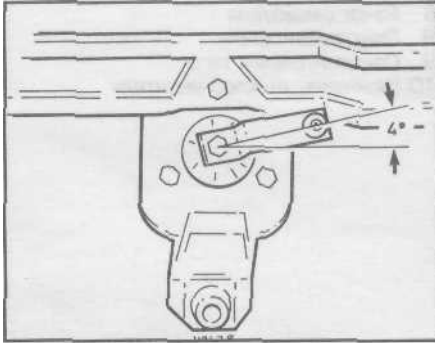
Угол коленчатого рычага ээлектродвигателя стеклоочистителя (двигатель в исходном положении)
